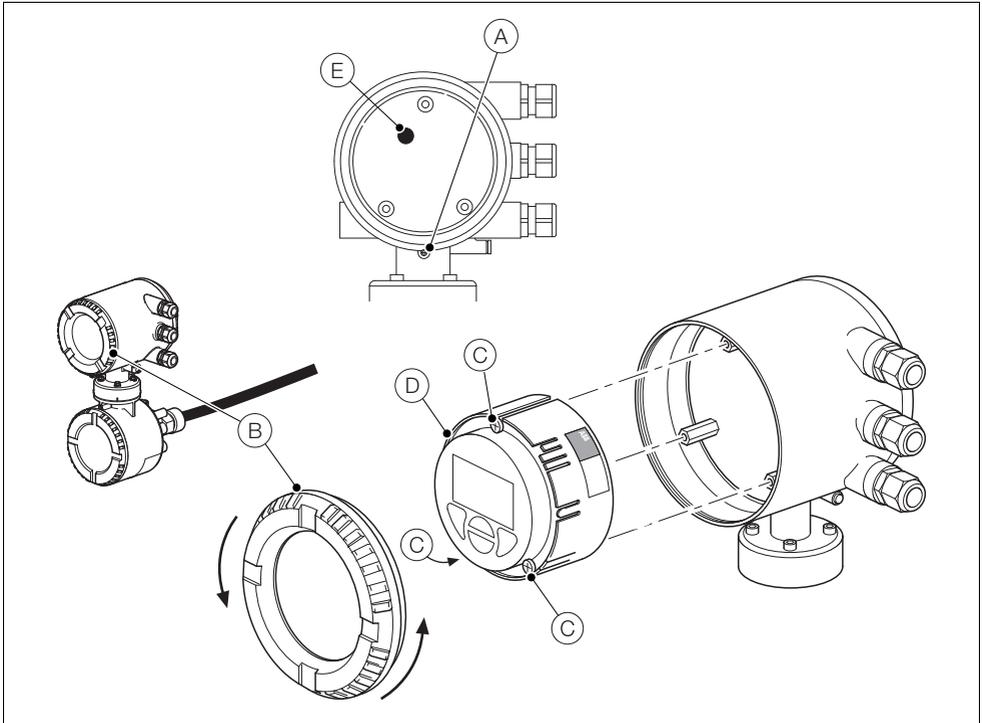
Externer Messumformer – Austausch der internen Sicherung
